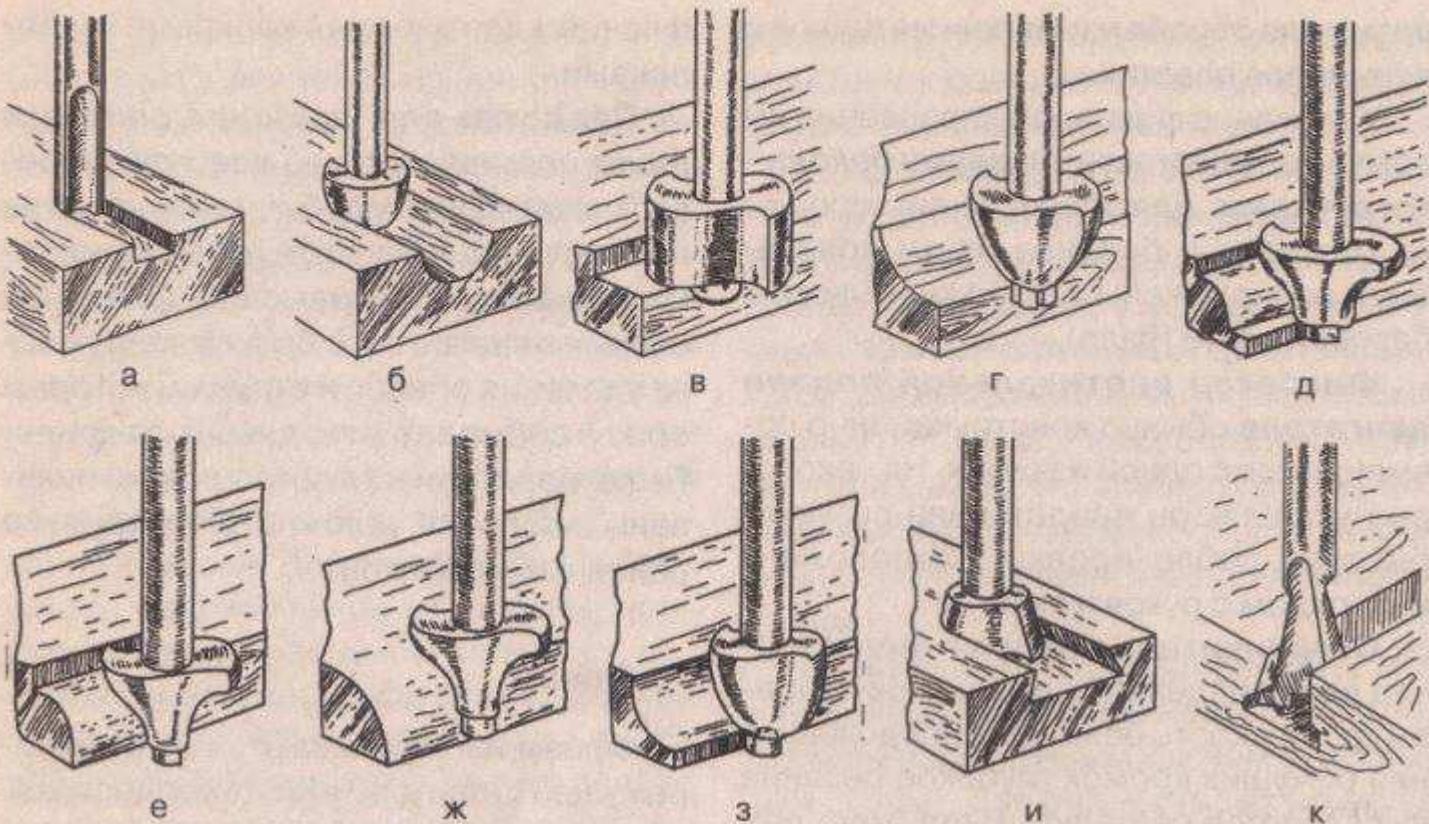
Виды фрез: а — пазовая (шпоночная) фреза; б — галтельная фреза; в — фреза на шарикоподшипниках с заходной шейкой для выборки фальца; г — фасонная фреза с заходной шейкой; д, е — фрезы для выборки четверти окружности; ж — профильная за круглительная фреза; з — галтельная фреза с заходной шейкой; и — шпоночно-шипорезная фреза; к — шипорезная фреза «ласточкин хвост»
